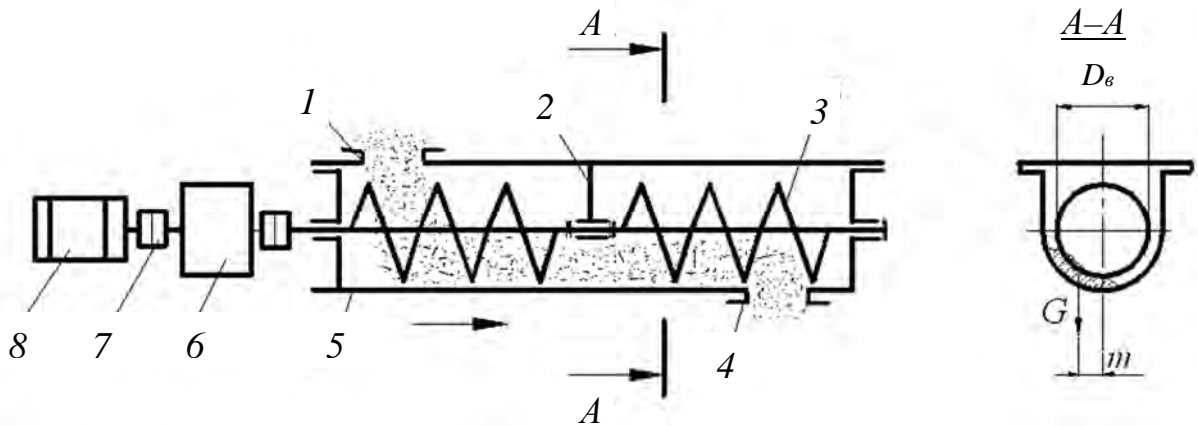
Схема горизонтального винтового конвейера: 1 – загрузочное устройство; 2 – подвесная промежуточная опора; 3 – винт; 4 – разгрузочное отверстие; 5 – желоб; 6 – муфта; 7 – редуктор; 8 – электродвигатель
